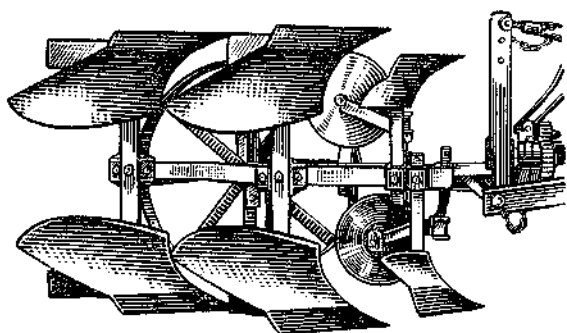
Плуг двухкорпусный оборотный навесной ПОН-2-30.
